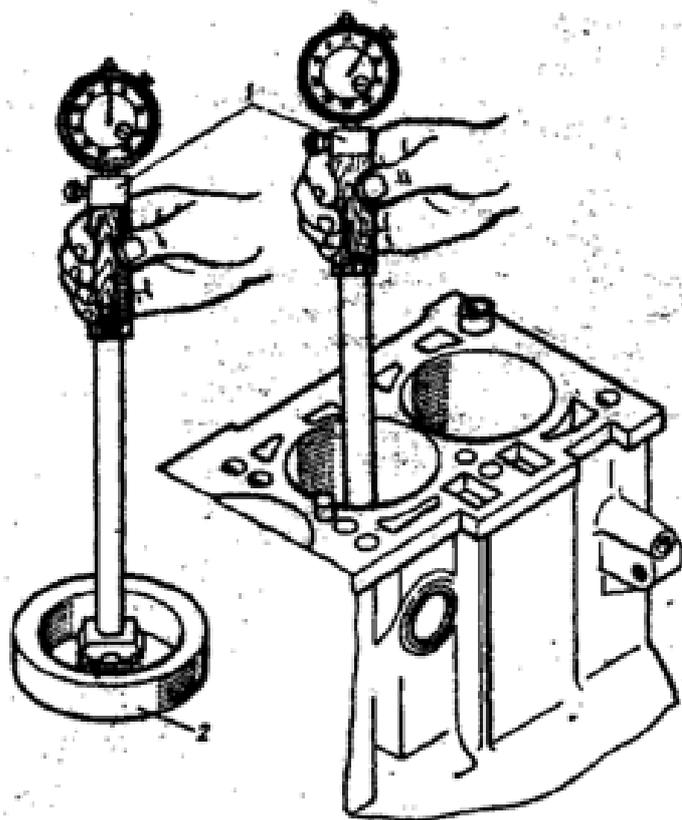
Замер диаметра цилиндра индикаторным нутромером: 1 - индикатор-нутромер; 2 - кольцо-калибр для установки нутромера на ноль
